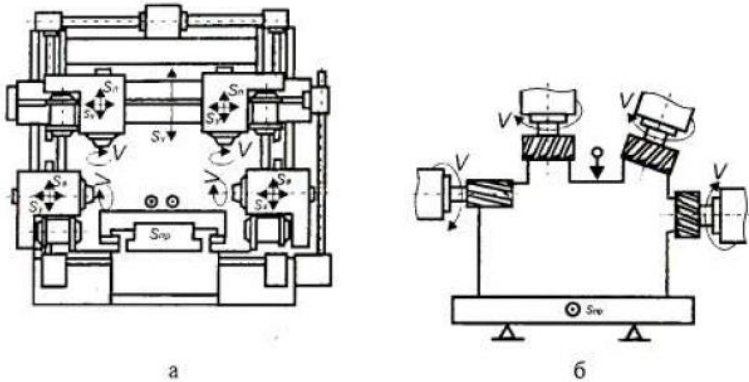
Загальний вигляд поздовжньо-фрезерного верстату (а) і схема фрезерування заготовки (б)
